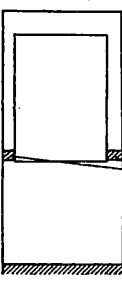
Zum Schweißen angespannte Bleche.
